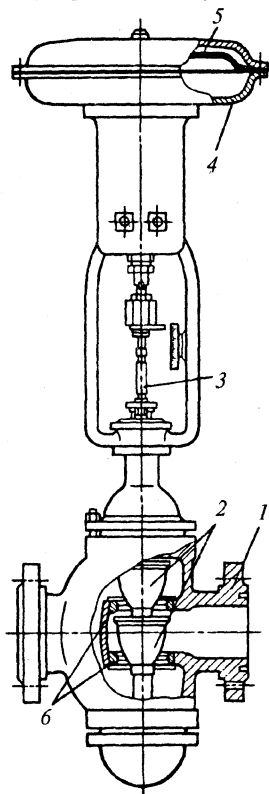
Регулирующий клапан с мембранным исполнительным механизмом:
